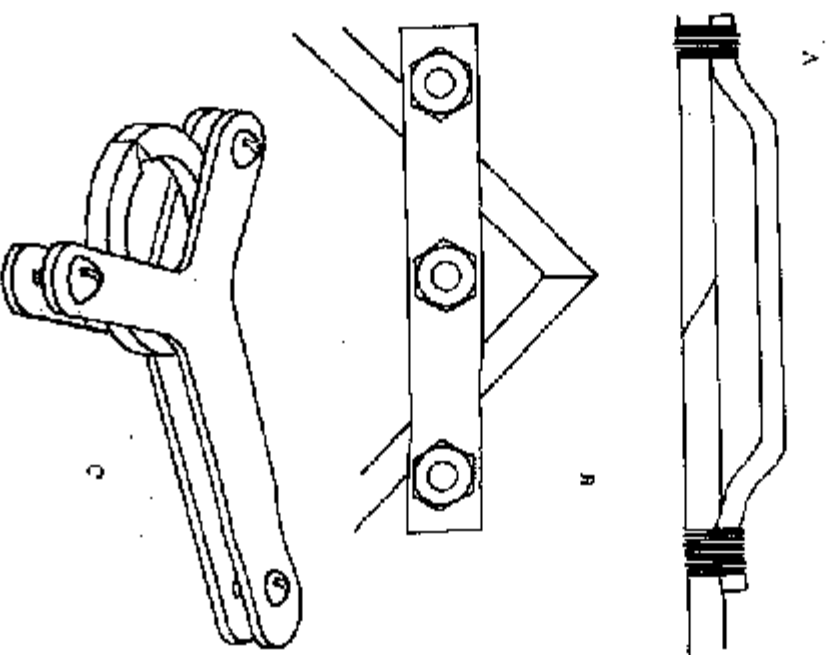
Las partes que serán unidas con soldadura fuerte deben ser mantenidas juntas por medio de artillos apropiados: (A) varilla de refuerzo y alambre de hierro; (B) partes atornilladas; (C) artillos de una abrazadera o prensa en Y.
